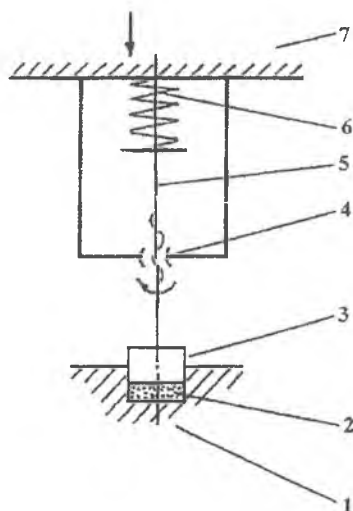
Штмп для формования порошковых деталей со скручиванием заготовки:
